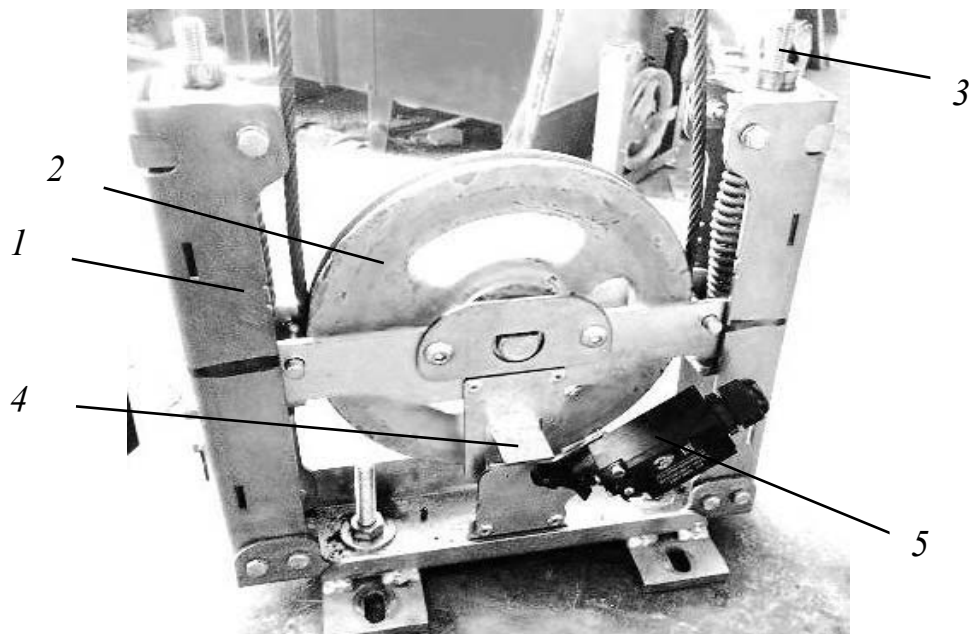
Опытный образец пружинного натяжного устройства (ОАО «Могилевлифтмаш»): 1 – корпус; 2 – шкив; 3 – шпилька; 4 – лыжа; 5 – выключатель
